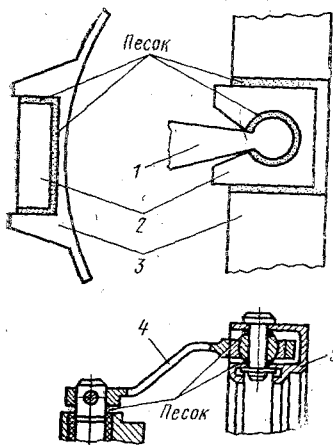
Места скопления песка и пыли в деталях системы поворота лопаток ВНА и НА 1, 2 и 3-й ступеней компрессора двигателя:
